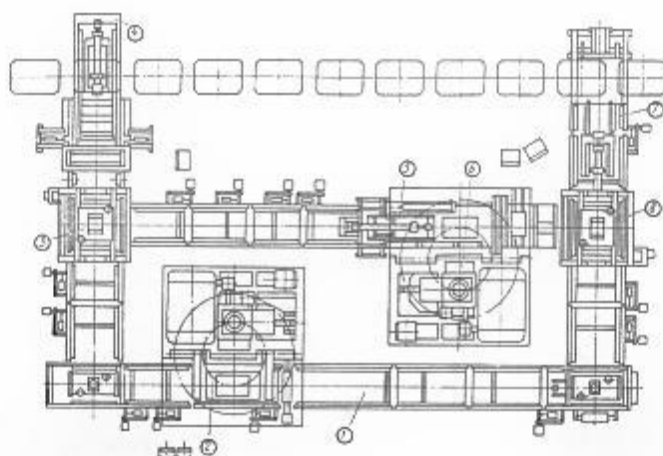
Автоматический формовочный модель модели AM20320 с двумя базовыми формовочными машинами (ВНИИЛИТМАШ): 1 – система транспорта; 2 – базовая формовочная машина модели 203Н20; 3 – механизм распаровки опок; 4 – механизм сталкивания пустых опок; 5 – механизм подачи опок; 6 – базовая формовочная машина модели 203В20; 7 – механизм выдачи готовых форм; 8 – механизм сборки форм.
